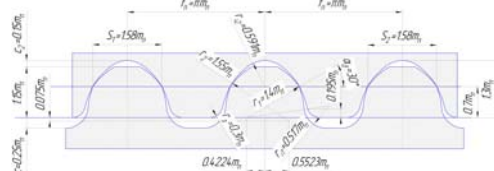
Исходные формообразующие контуры для зубчатого колеса и шестерни зубчатой передачи с профилем Новикова
